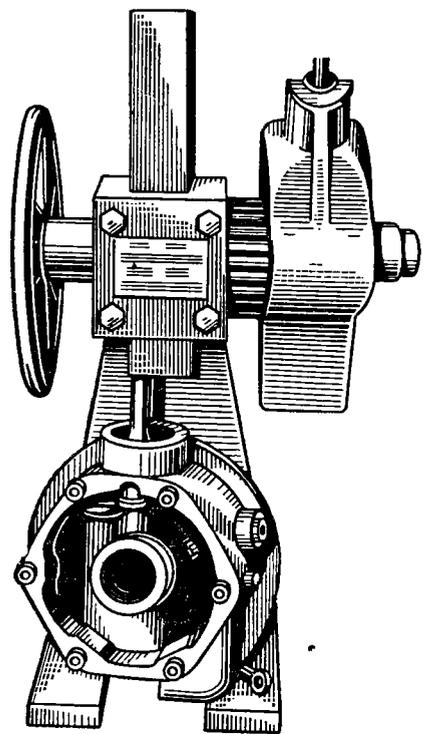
Запрессовка ведущей шестерни с подшипниками в гнездо картера.
